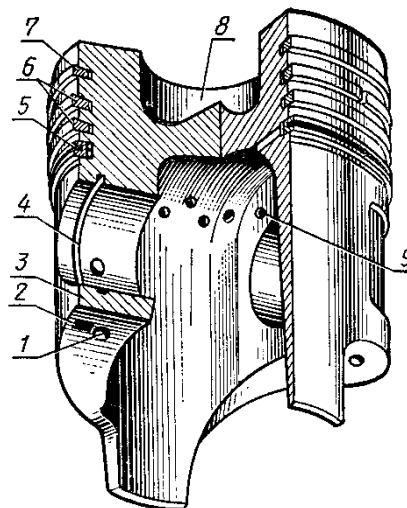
а. Поршень дизеля:1 – отверстие для смазки поршневого пальца; 2 – метка размерной группы; 3 – бобышка поршня; 4 – канавка для стопорного кольца; 5 – маслосъемное кольцо; 6 и 7 – компрессионные кольца; 8 – камера сгорания; 9 – отверстия для отвода масла
